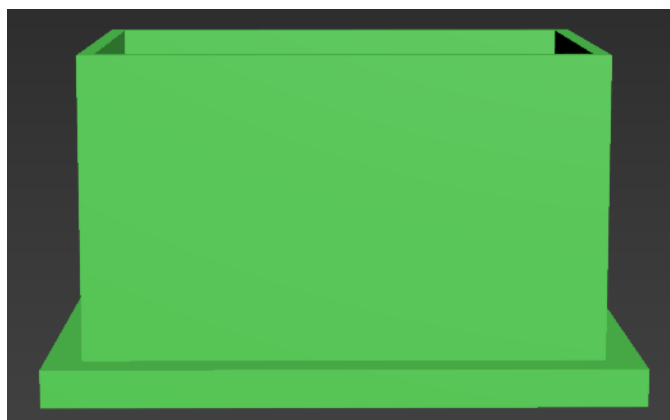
Встановлення борту внутрішньої деталі
